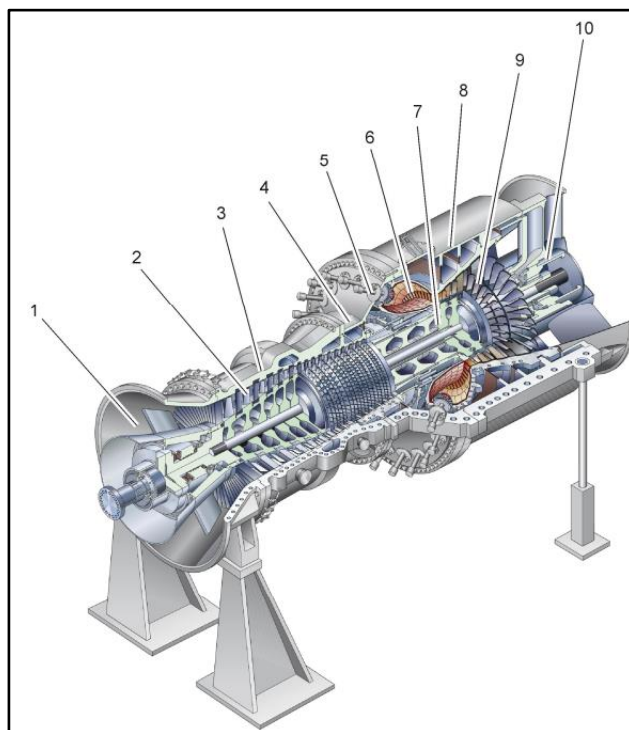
Vue d'ensemble turbine TG SGT5-4000F
